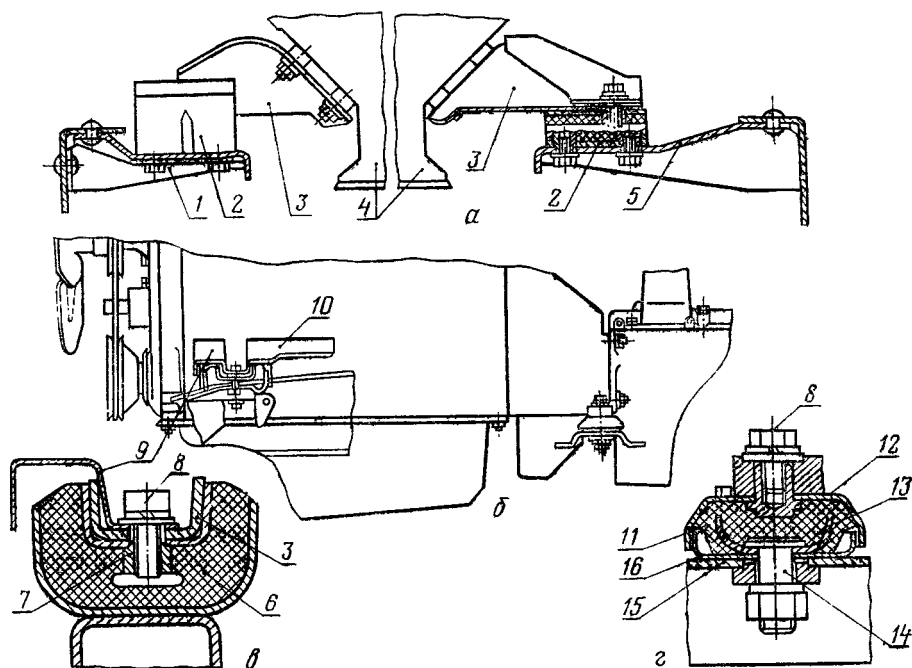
Крепление двигателя ГАЗ-53 к раме:
